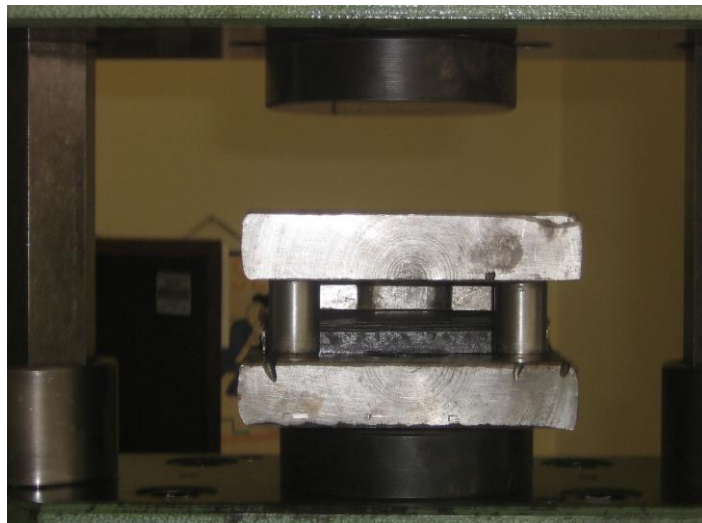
Matriz colocada en máquina de ensayos universales.
